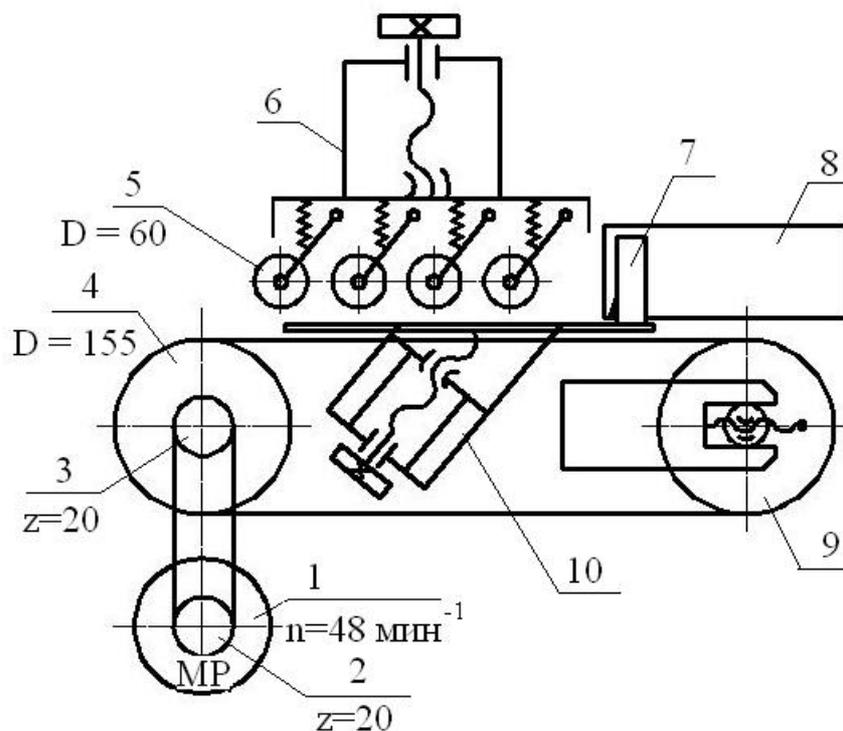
Кинематическая схема механизмов торцового пресса в зоне загрузки заготовок
